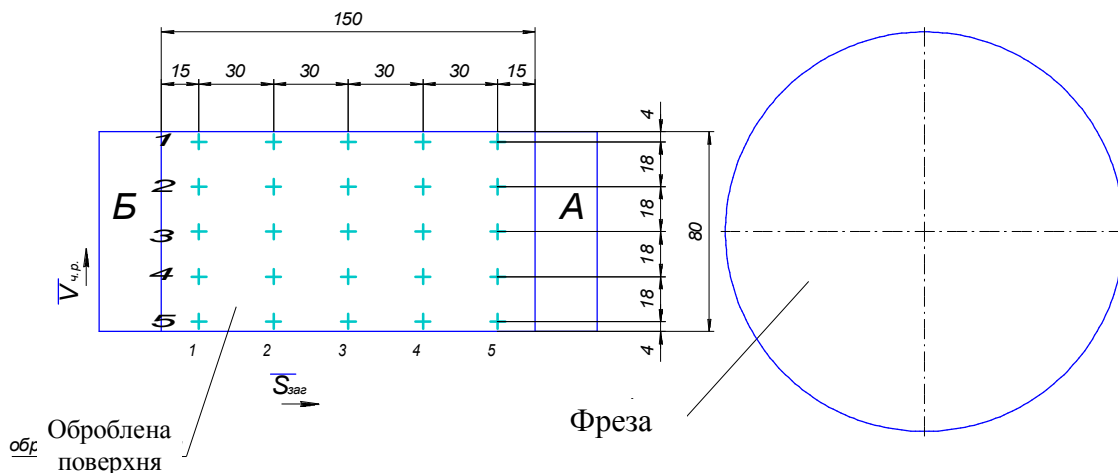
Схема виміру шорсткості обробленої поверхні заготовки
